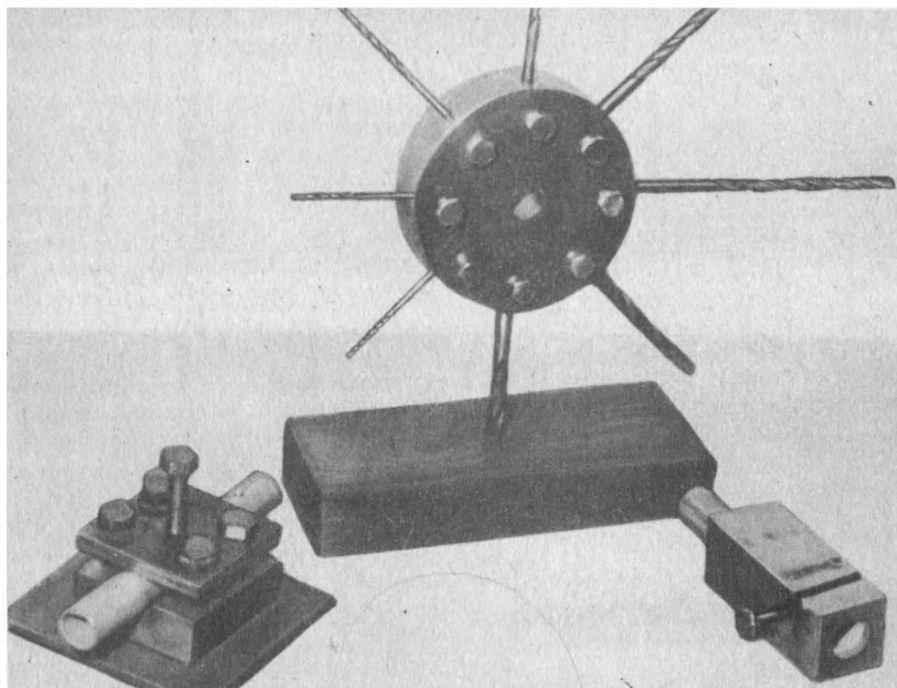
Приспособления: для сверления отверстий в трубках; для токарного станка ТВ-4; для фрезерного станка — обрезка колец и ручек напильников.
